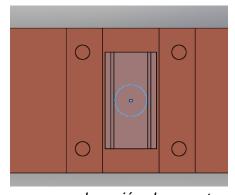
Barreno para colocación de resorte en la barra paralela.
